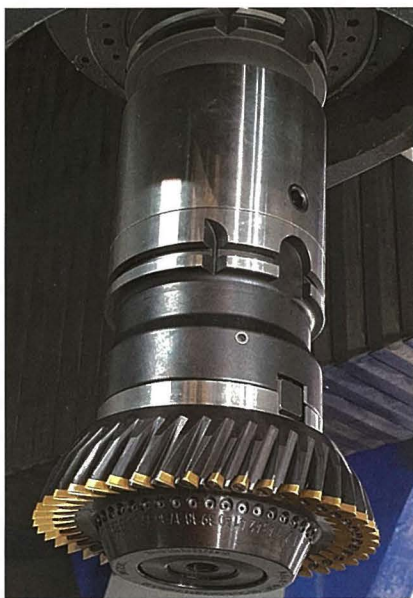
Das Fräswerkzeug ist in der Schleifspindel gespannt, das Werkstück dreht sich auf dem Maschinentisch synchron dazu. Foto: Ingersoll
